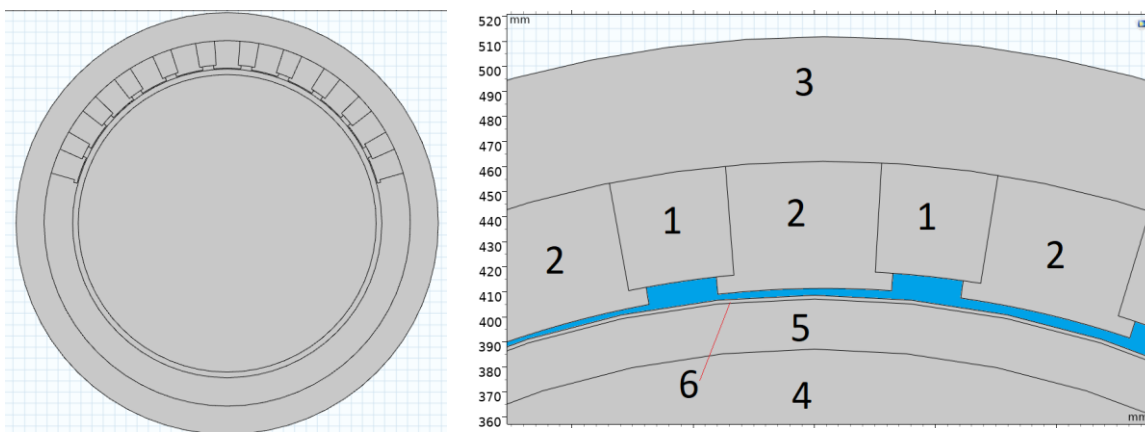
Магнитный подшипник: 1 – неодимовые магниты; 2 – прослойки из стали с высокой магнитной проницаемостью; 3 – дейдвудная труба; 4 – основной вал; 5 – облицовка из стали с высокой магнитной проницаемостью; 6 – облицовка из коррозионно – стойкой стали.
